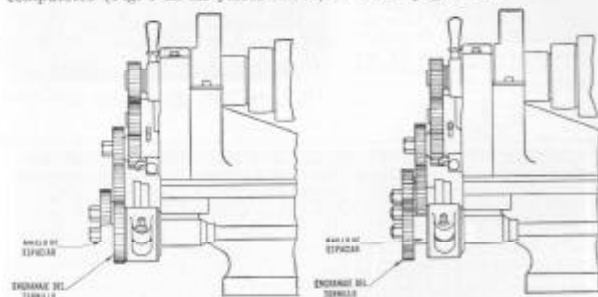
A. Posición del anillo de espaciar para engranajes simples
